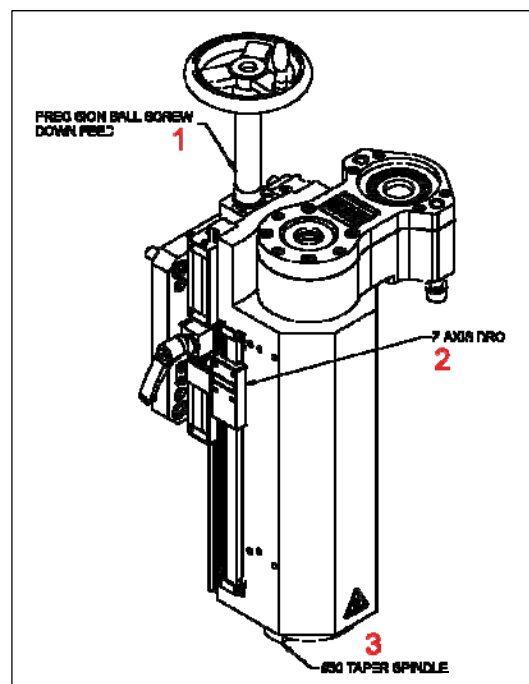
Компоненты фрезерной головки (кат. № 72277)
